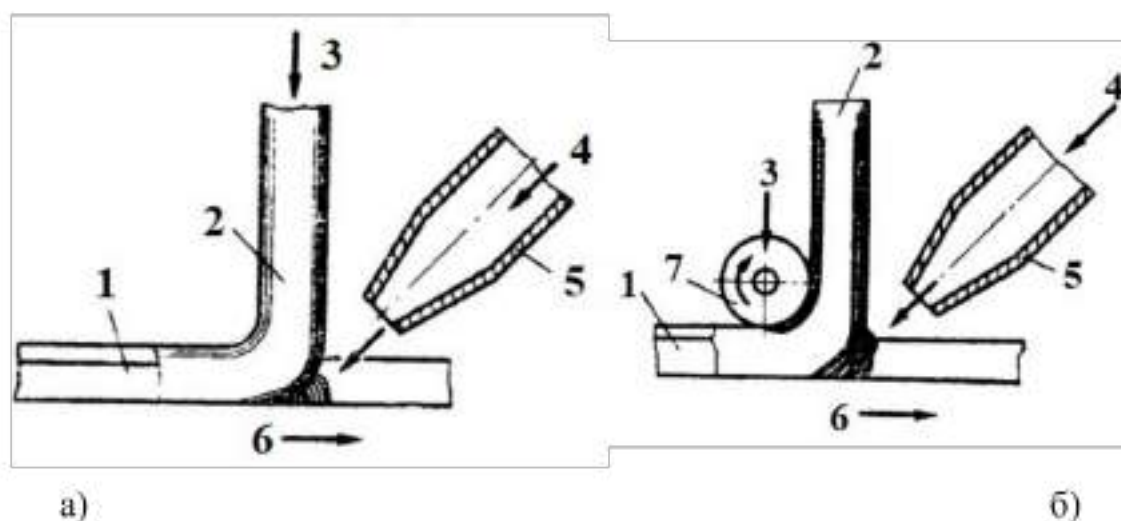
Зварювання нагрітим газом з присадним прутком (а) та прикочуванням (б): 1 – деталь, що зварюється; 2 – присадковий пруток; 3 – зусилля; 4 – нагрітий газ; 5 – сопло; 6 – напрямок зварювання; 7 – натискний ролик
